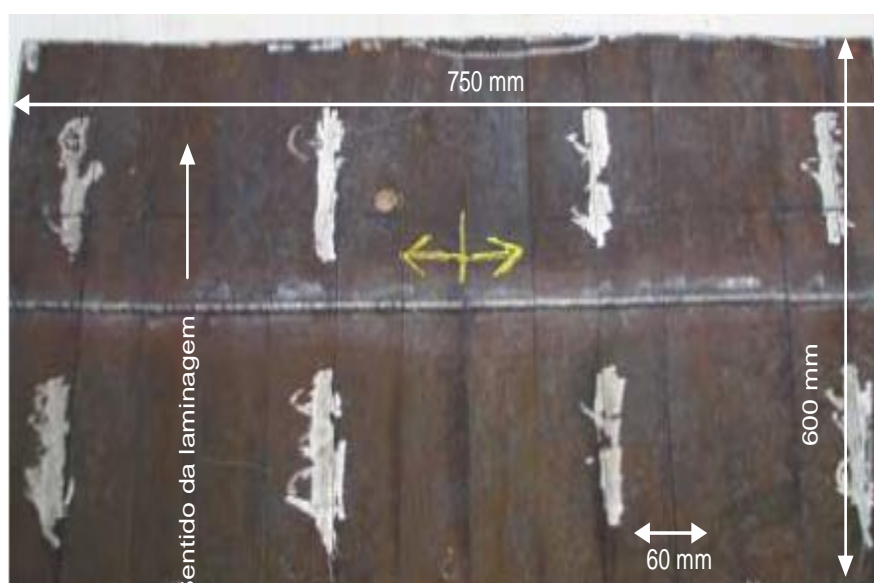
Dimensões dos provetes soldados para ensaio de fadiga
